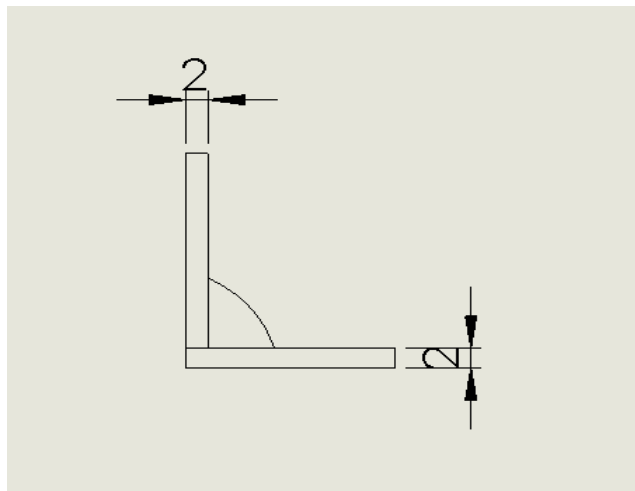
Diseño de junta soldada para placas de 2 mm. Fuente:
